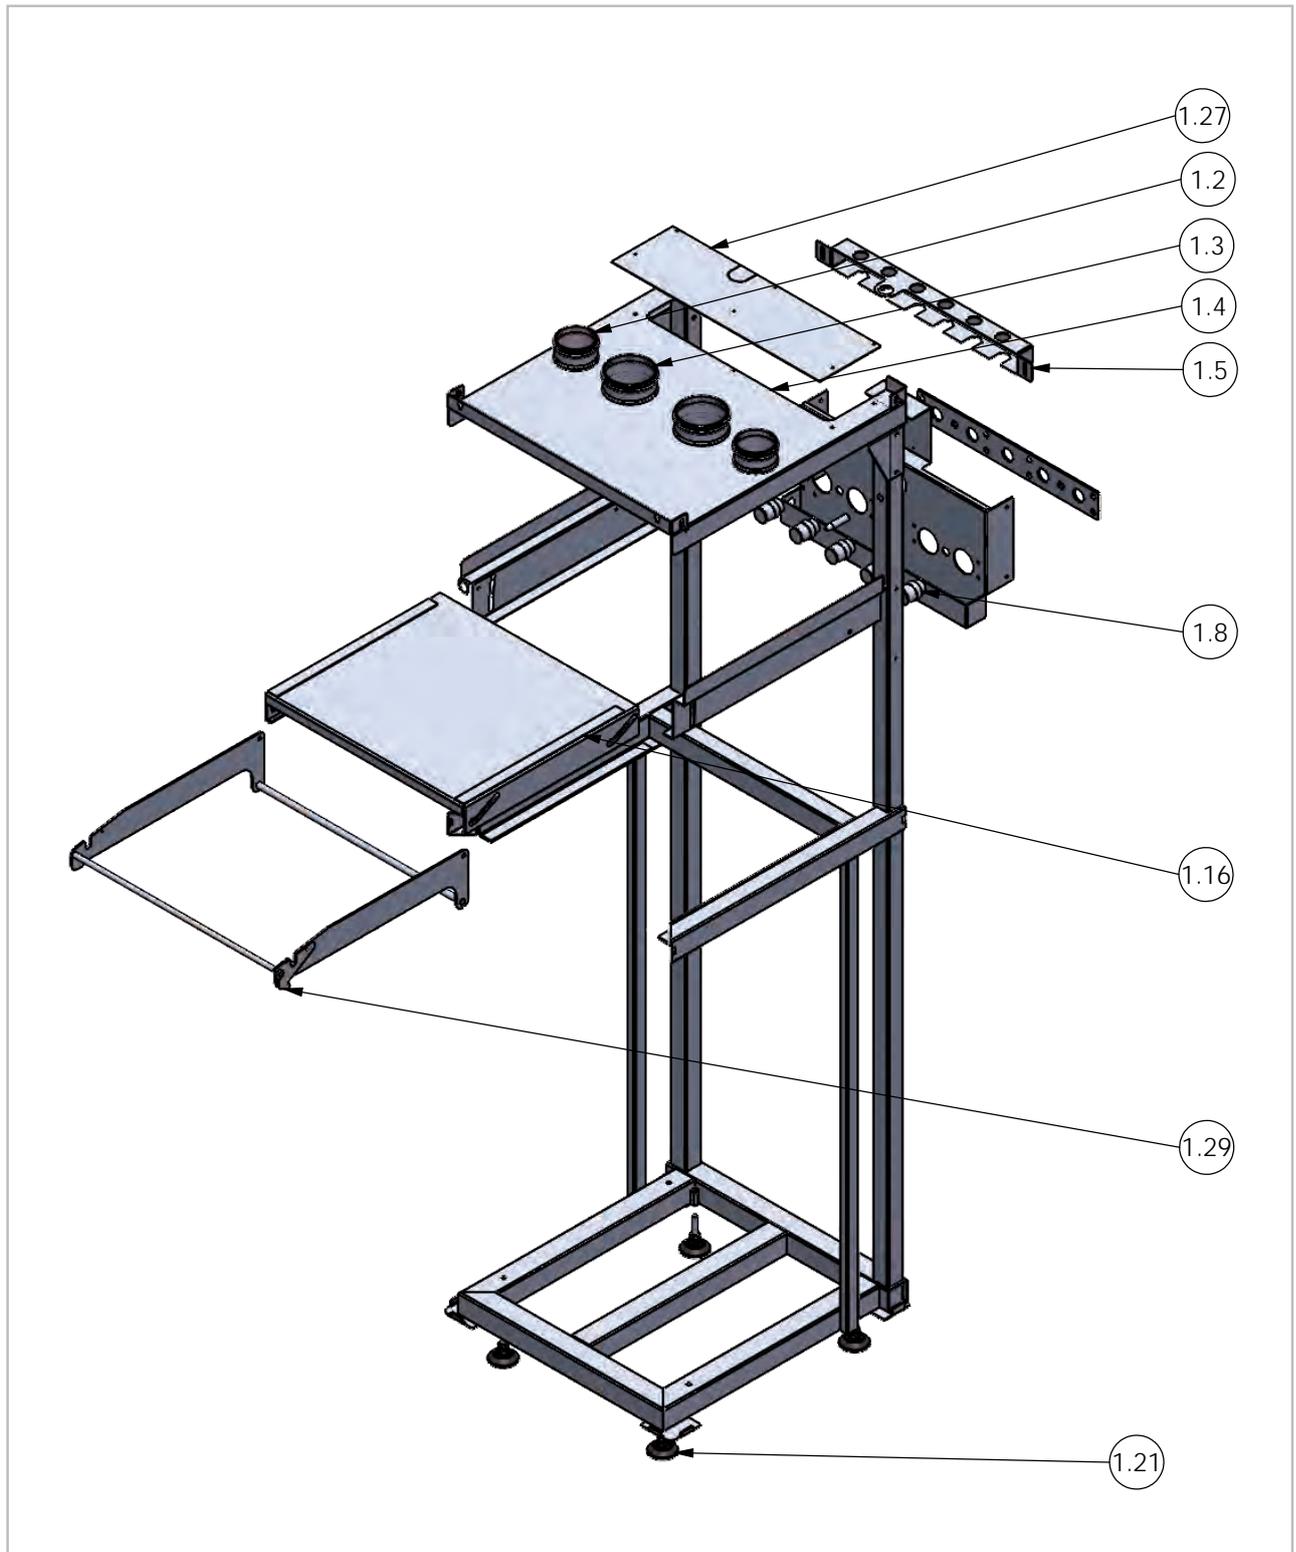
Explosionszeichnung Gestell mit Anbauteilen
